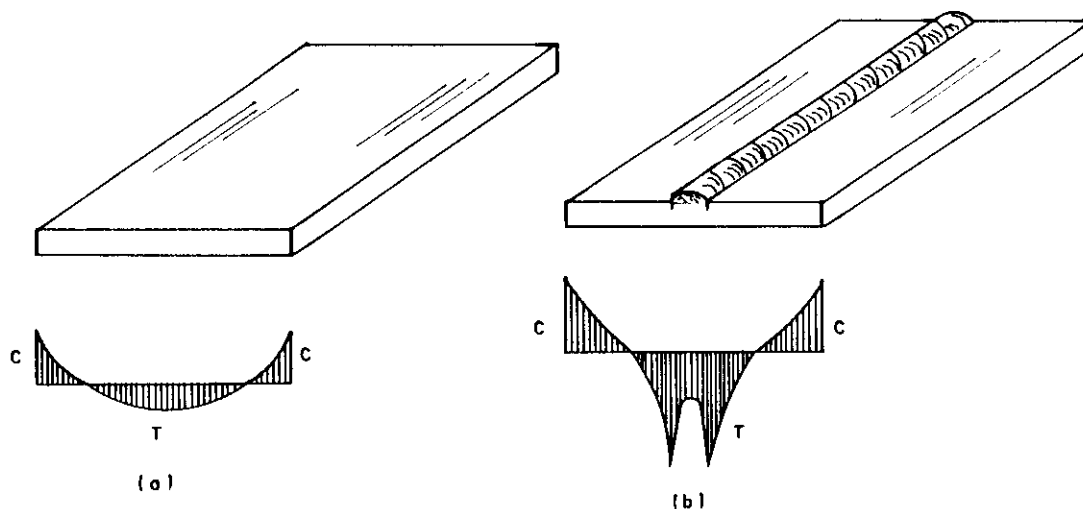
Tensões residuais em chapa laminada: (a) tensões residuais no topo da superfície, antes da soldagem e (b) tensões residuais no topo da superfície após a soldagem.
